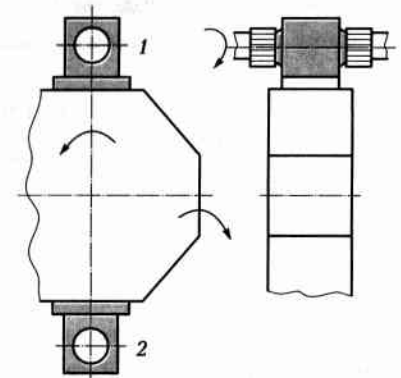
Схема обработки на барабанно-фрезерном станке двух параллельных плоскостей
